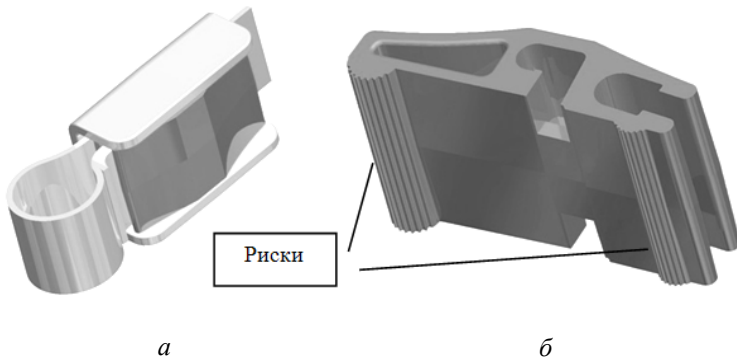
3D-модель изделия «Зажим хирургический»: *а* – изделие в сборе; *б* – пластмассовая деталь (отливка), на которую необходимо спроектировать и изготовить пресс-форму
